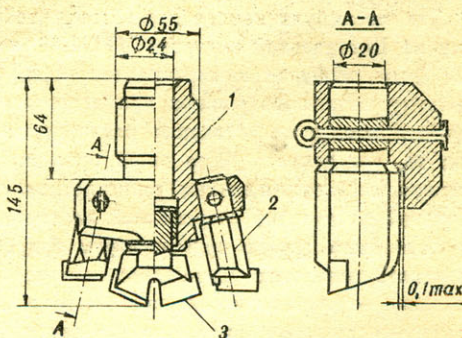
Схема бура: 1 — корпус, 2 — вставные резцы, 3 — сменный забурник.
